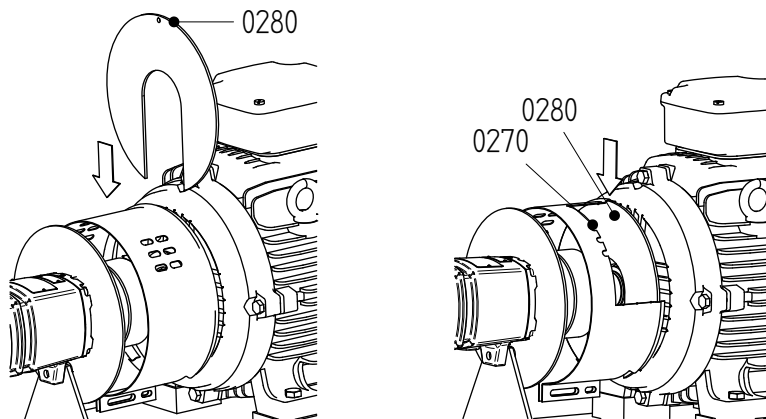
Montieren der Montageplatte auf der Motorseite.
